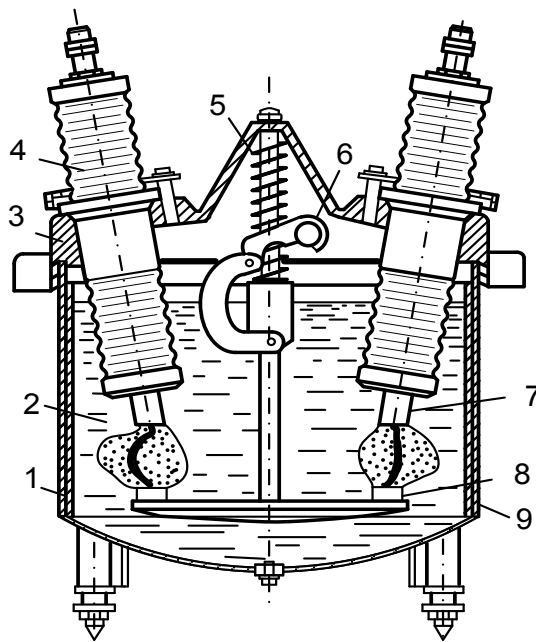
Конструктивна схема оливного бакового вимикача:
